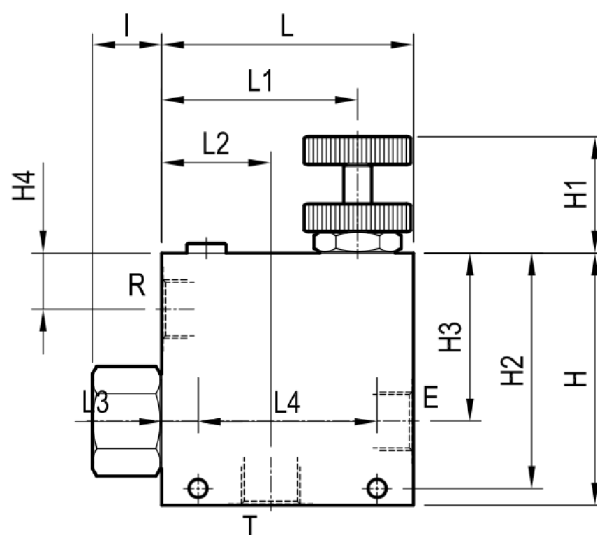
Řez škrťícím ventilem A-VRFC3 [28]
